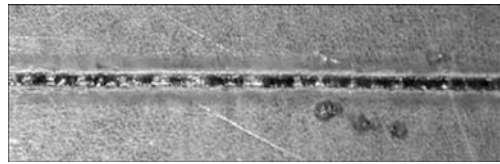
Вид сварного шва оцинкованных стальных листов в конструкции с соединением внахлестку с нулевым зазором
